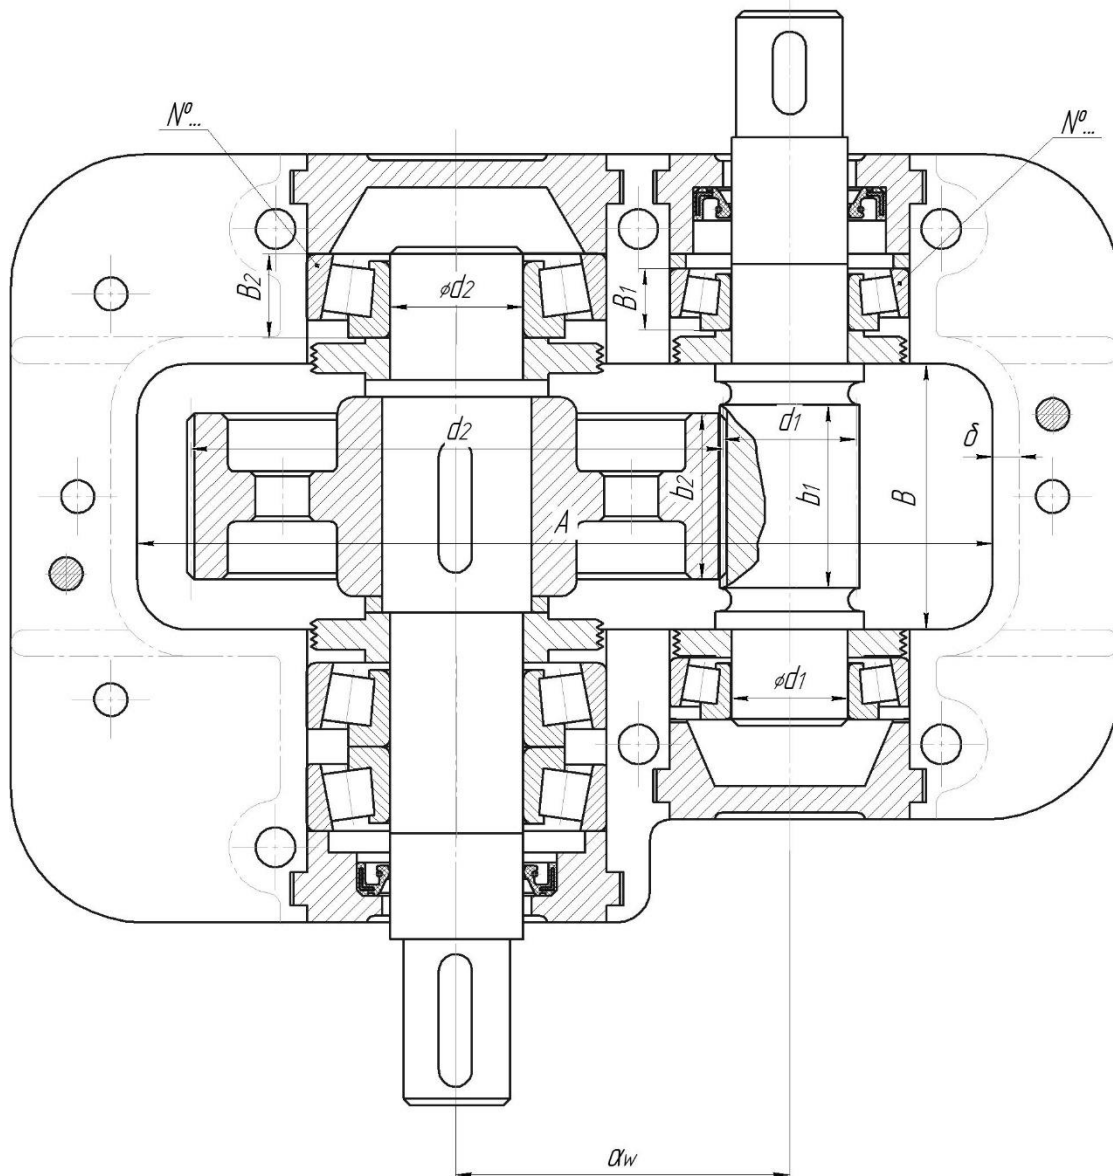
Циліндричний одноступеневий косозубий редуктор
